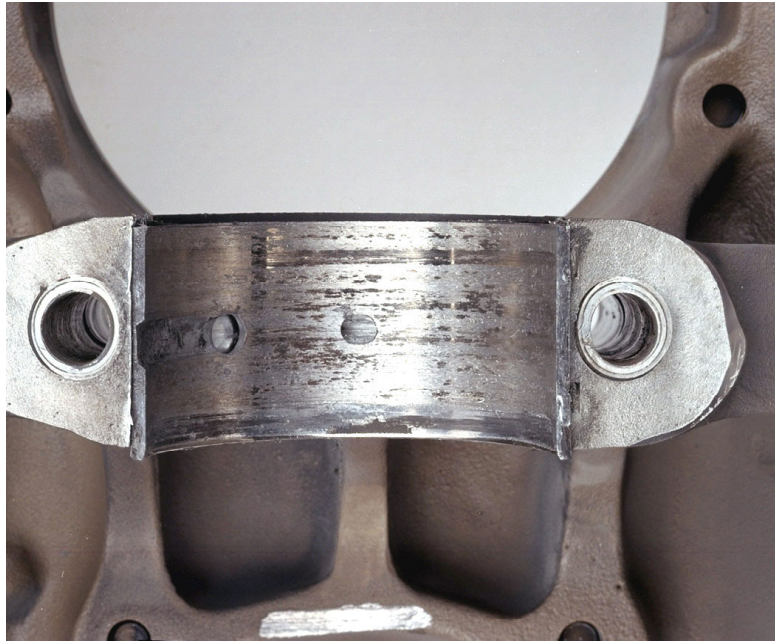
Coussinet du palier central, décalé vers l'arrière (vers le bas sur la photographie) ; Traces de fretting sur le plan de joint.
